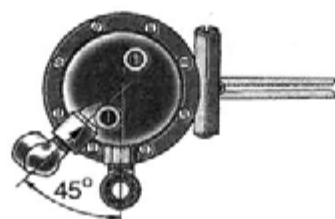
Положение головки и крышки топливного насоса относительно корпуса
